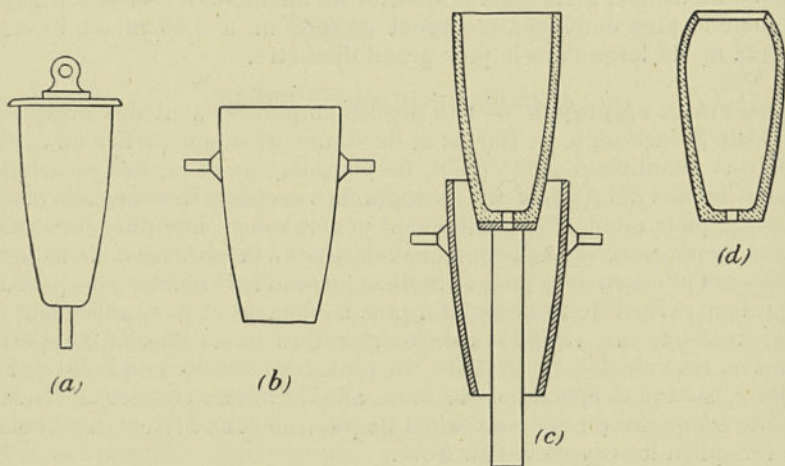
Moule et mandrin pour fabriquer les creusets à la main.
